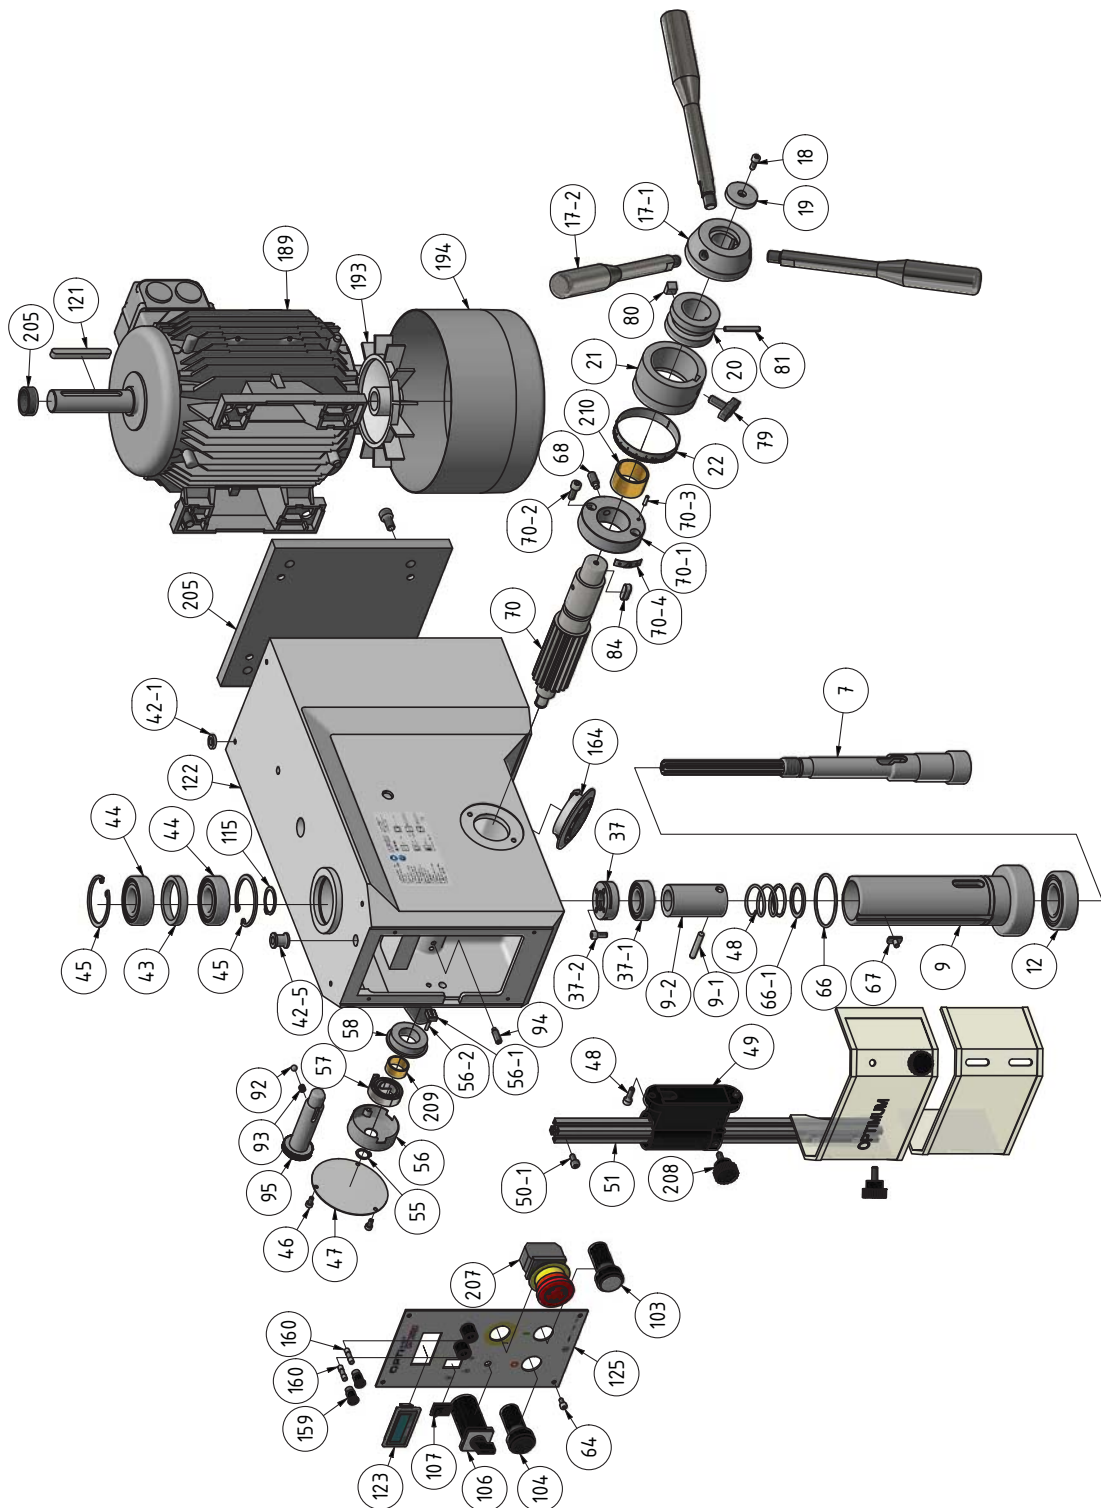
Bohrkopf DH28BV - Drilling head DH28BV
